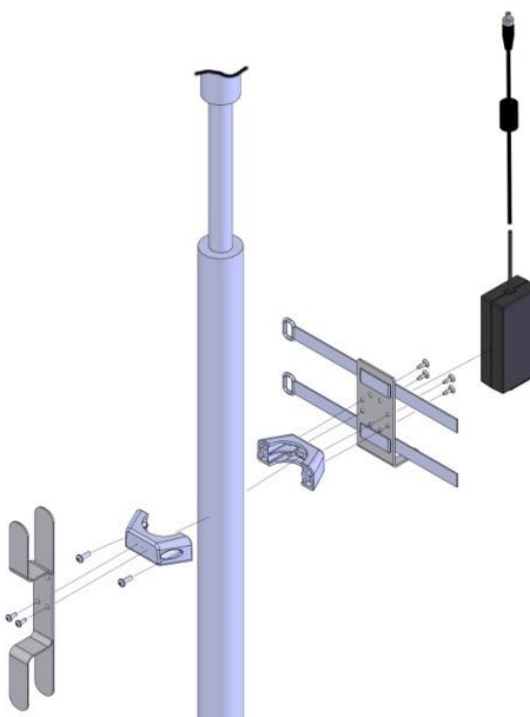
Fixar o suporte de montagem do adaptador de energia/cabo
